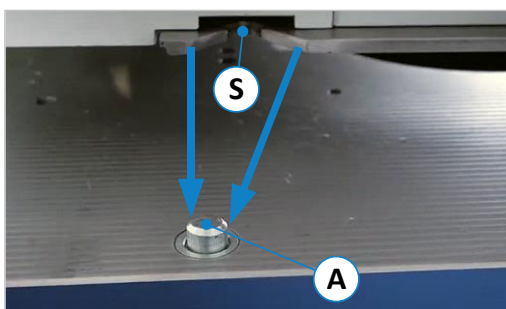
aligner le réceptacle sur le boulon d'arrêt
